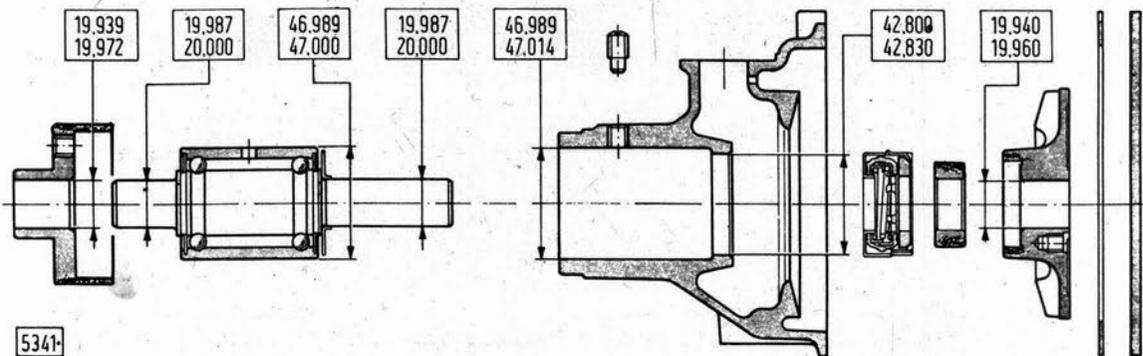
Dimensions principales des pièces de la pompe à eau en mm.
